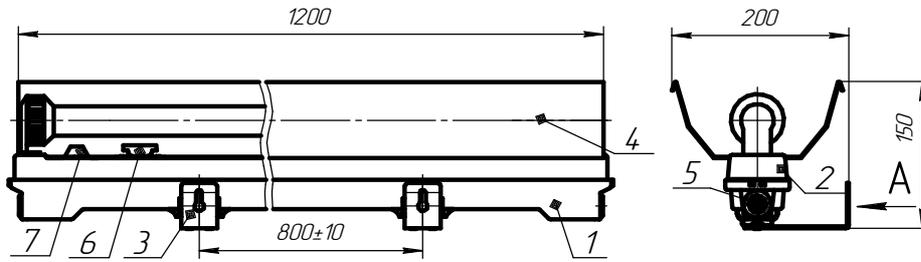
1. Корпус в сборе; 2. Панель в сборе; 3. Узел подвеса; 4. Отражатель; 5. Заглушка; 6. Рукоятка; 7. Рукоятка.
